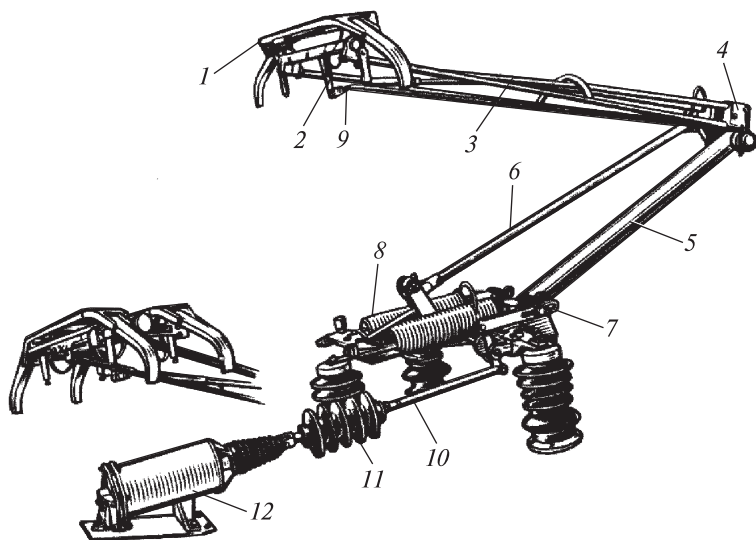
Асимметричный токоприемник универсального назначения: 1 — каретка полоза; 2 — стержень; 3 — верхняя рама; 4 — поперечный кронштейн; 5, 6 — рычаги; 7 — кронштейн; 8 — пружина; 9 — тяга; 10 — поворотный вал; 11 — изолятор; 12 — пневмоцилиндр
